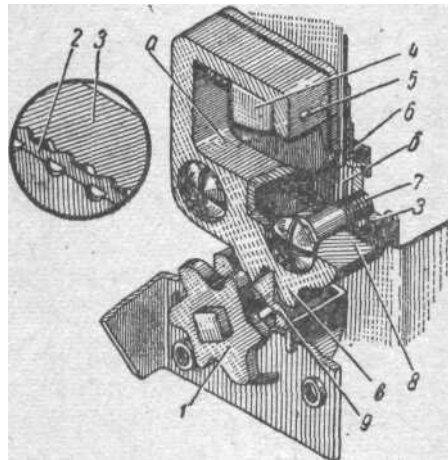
Зашелка замка двери и сопрягающиеся с ней детали замка:
